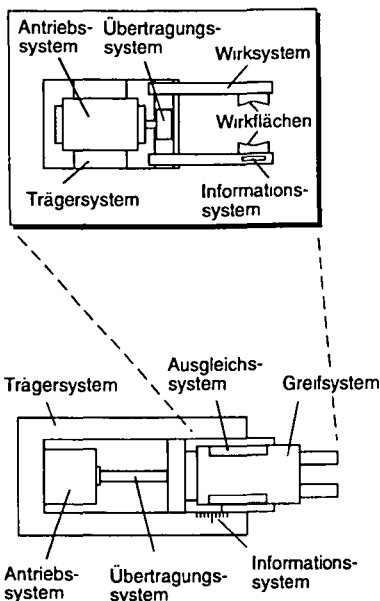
Teilsysteme von Greifern und Montagewerkzeugen
